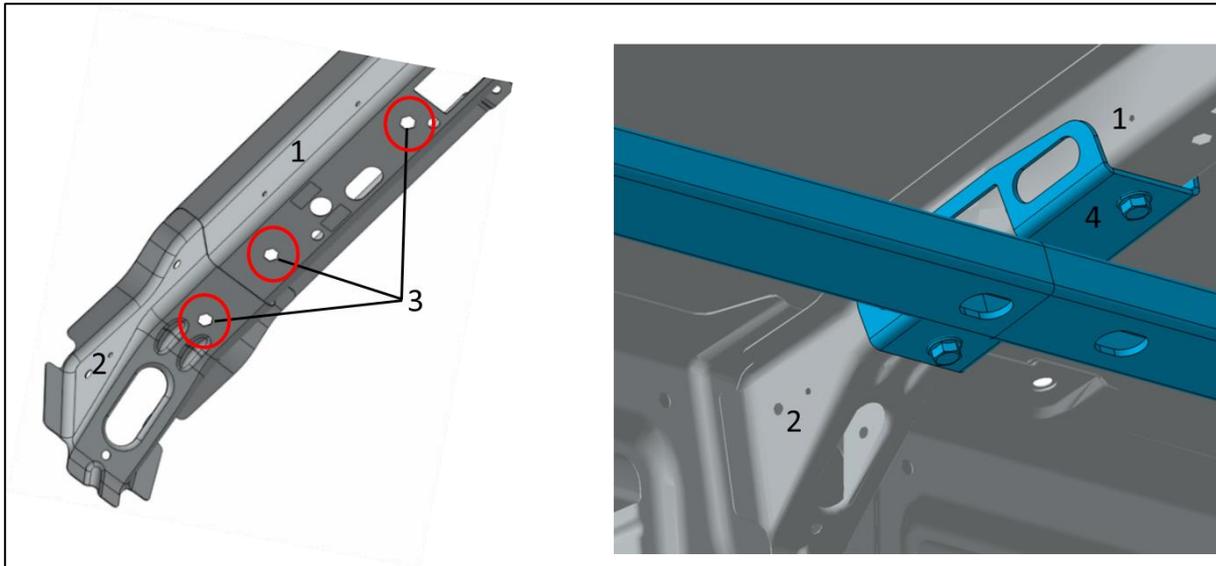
esempio di "montaggio del profilato longitudinale sul tetto"
